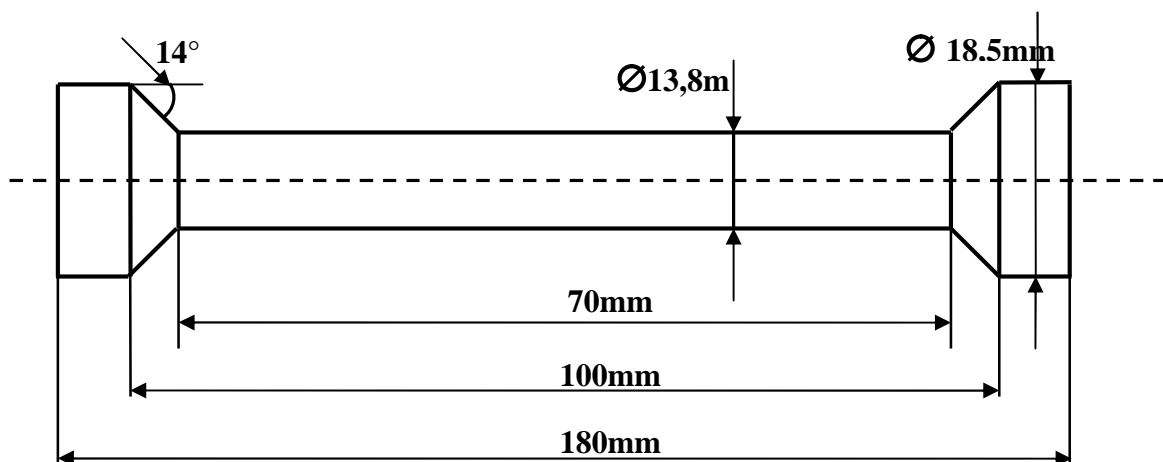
Formes et dimensions des éprouvettes de traction coulées en sable
